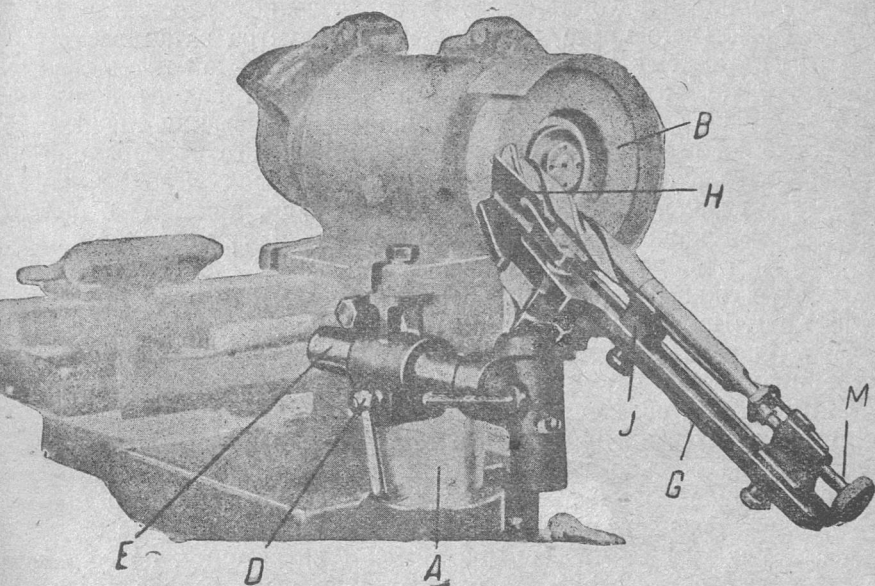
Точильный станок с приспособлением для заточки сверл по принципу Уошборн.
